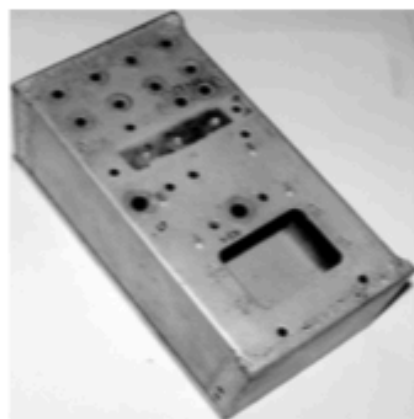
Вид заготовки из шасси блока усиления мощности радиостанции “Кама-С”. Собственно, это уже – готовый корпус. Торцевые стенки, вырезанные из крышек шасси оконечного каскада радиостанции, припаяны к заготовке, образуя коробку. Снизу – ещё одна крышка эту коробку закрывает
